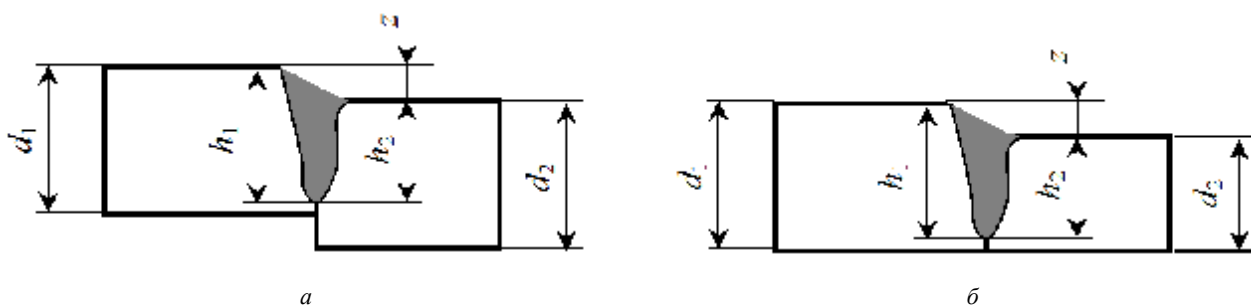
Виды превышения кромок: а – неточность сборки ($d_1 = d_2$); б – сварка деталей разной толщины ($d_1 \neq d_2$)
